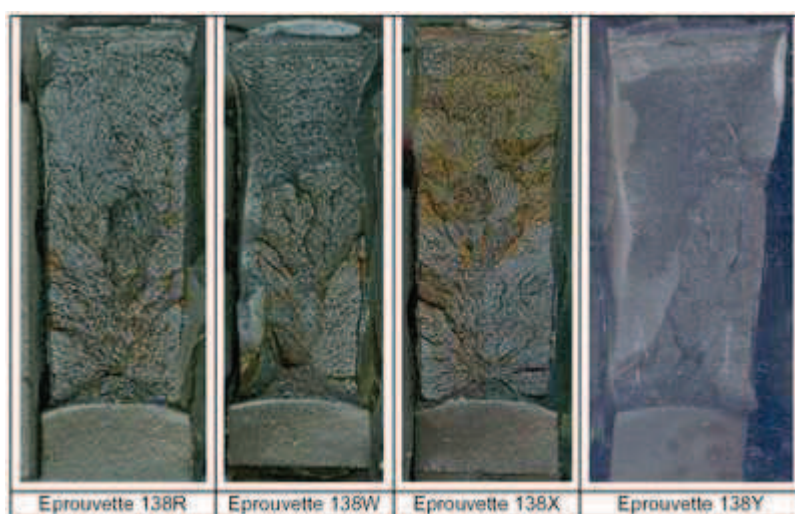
Macrographies des faciès de rupture - éprouvettes CT testées à -50°C
